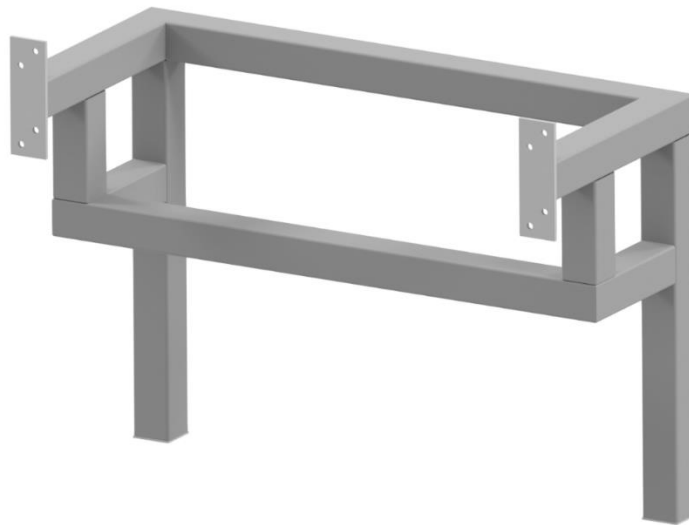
Propuesta de diseño estructura de las ruedas de tracción.
